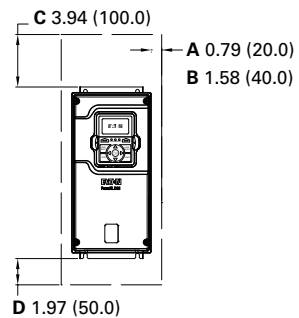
Desen dimensiuni montare pe contrapanou FR1
